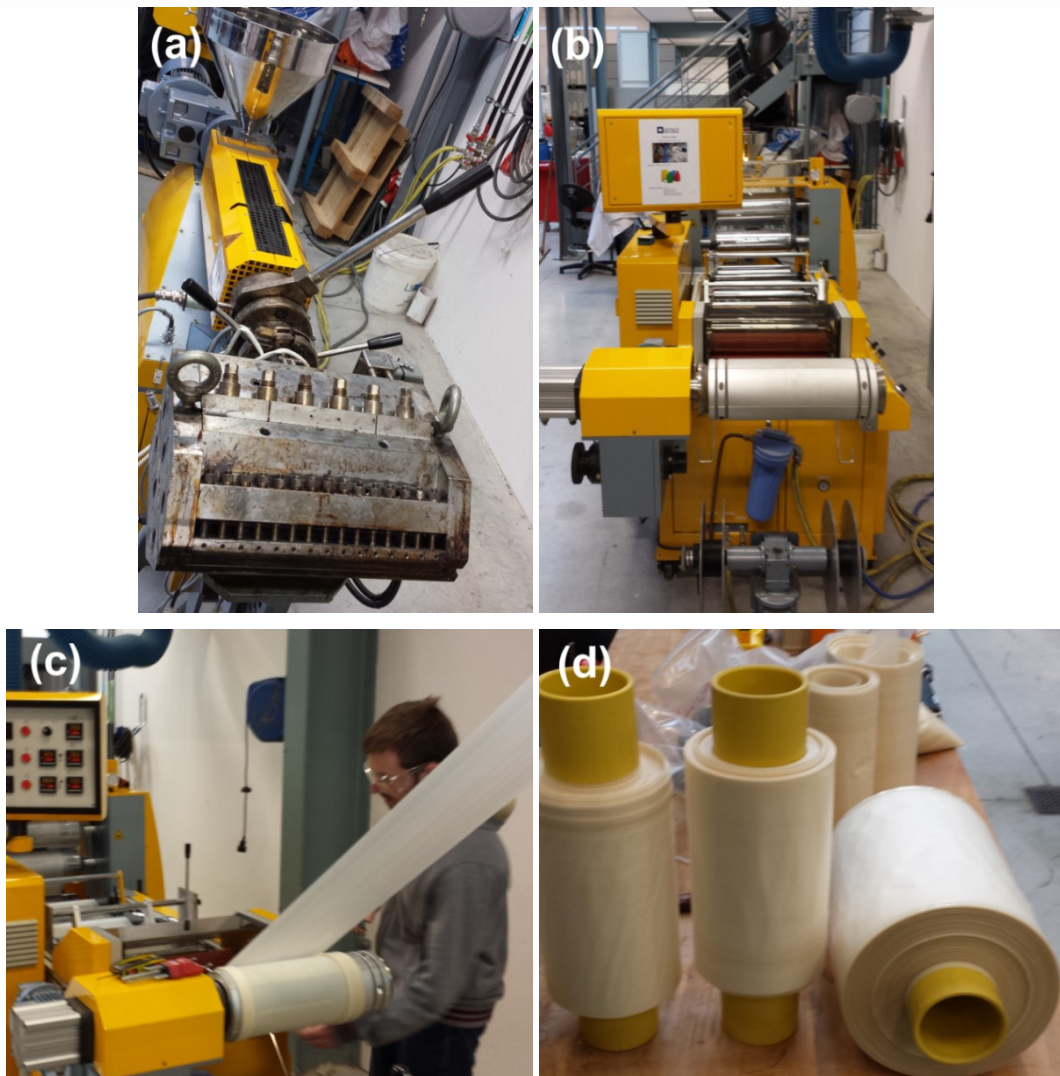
(a) Extrudeuse monovis Labtech Engineering 30 mm 30D et filière plate 350 mm, (b) Calandreuse, (c) Découpe des lisières du film et (d) Bobines réalisées
